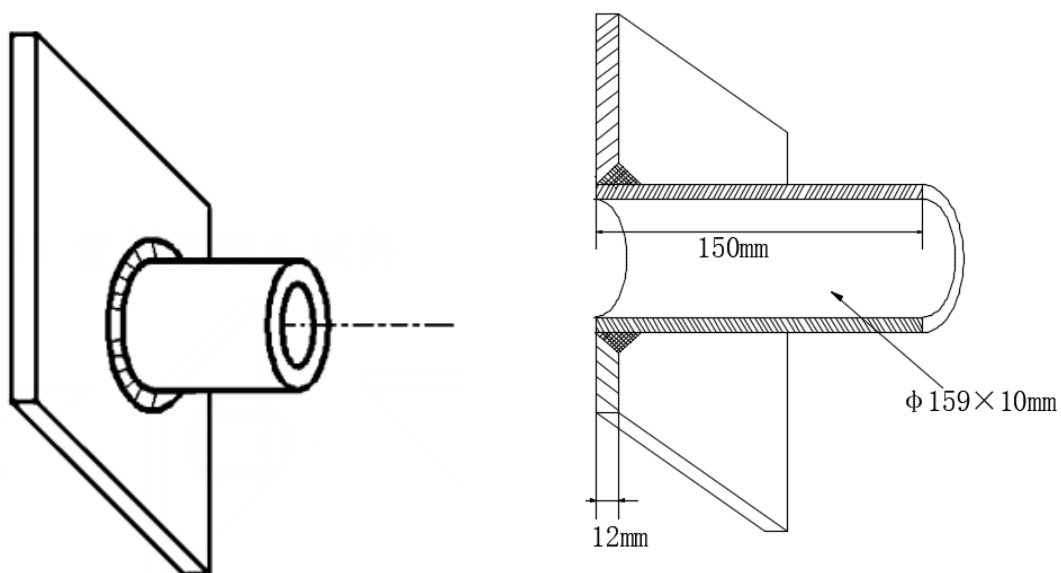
磁粉检测——管板直插式角接试件位置及尺寸
